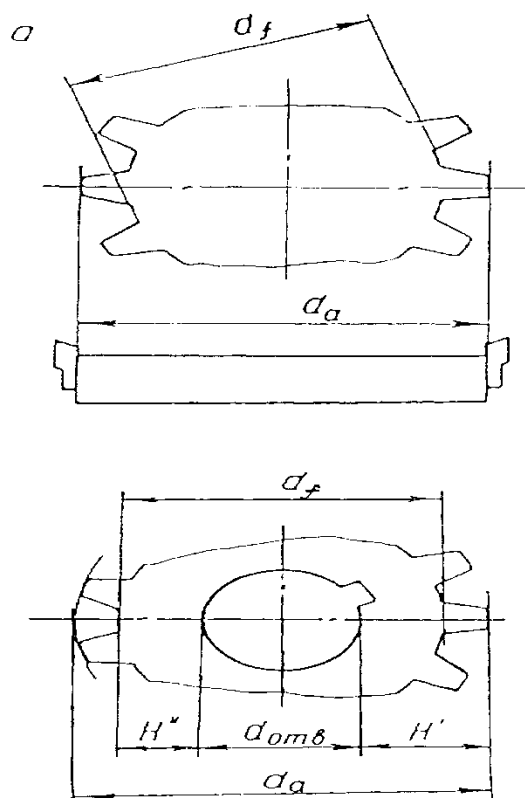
Схема обмера диаметров вершин (d_a) и впадин (d_f) зубчатого колеса:
